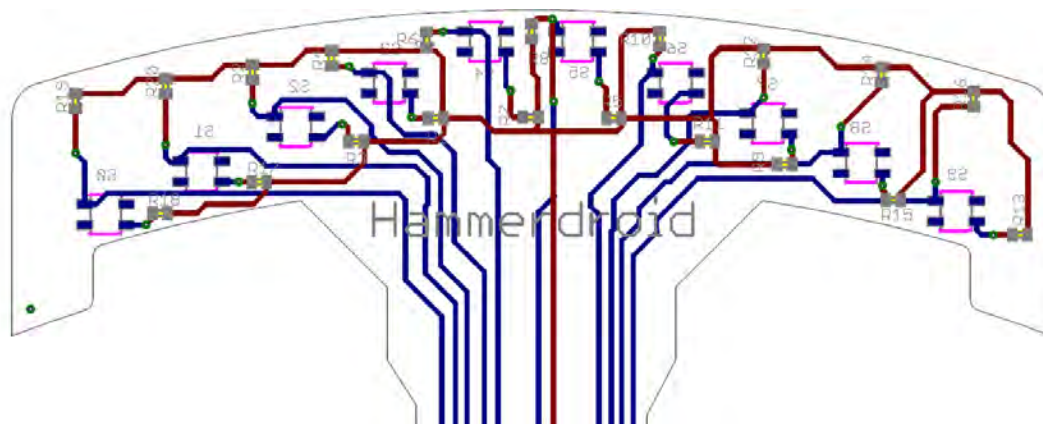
Parte superior del PCB que contiene los sensores ópticos
